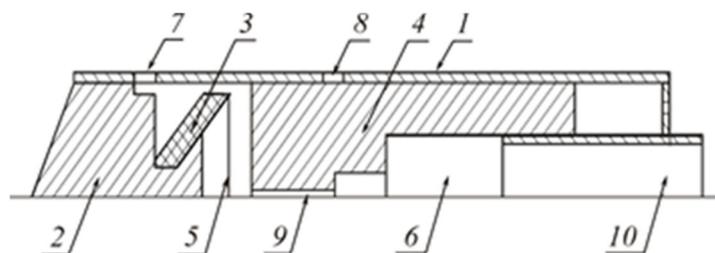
Принципиальная схема ударной машины: 1 — корпус; 2 — наковальня; 3 — клапан; 4 — боек; 5 — камера обратного хода; 6 — камера прямого хода; 7 — первое выхлопное отверстие; 8 — второе выхлопное отверстие; 9 — межкамерный дроссель; 10 — подача воздуха
